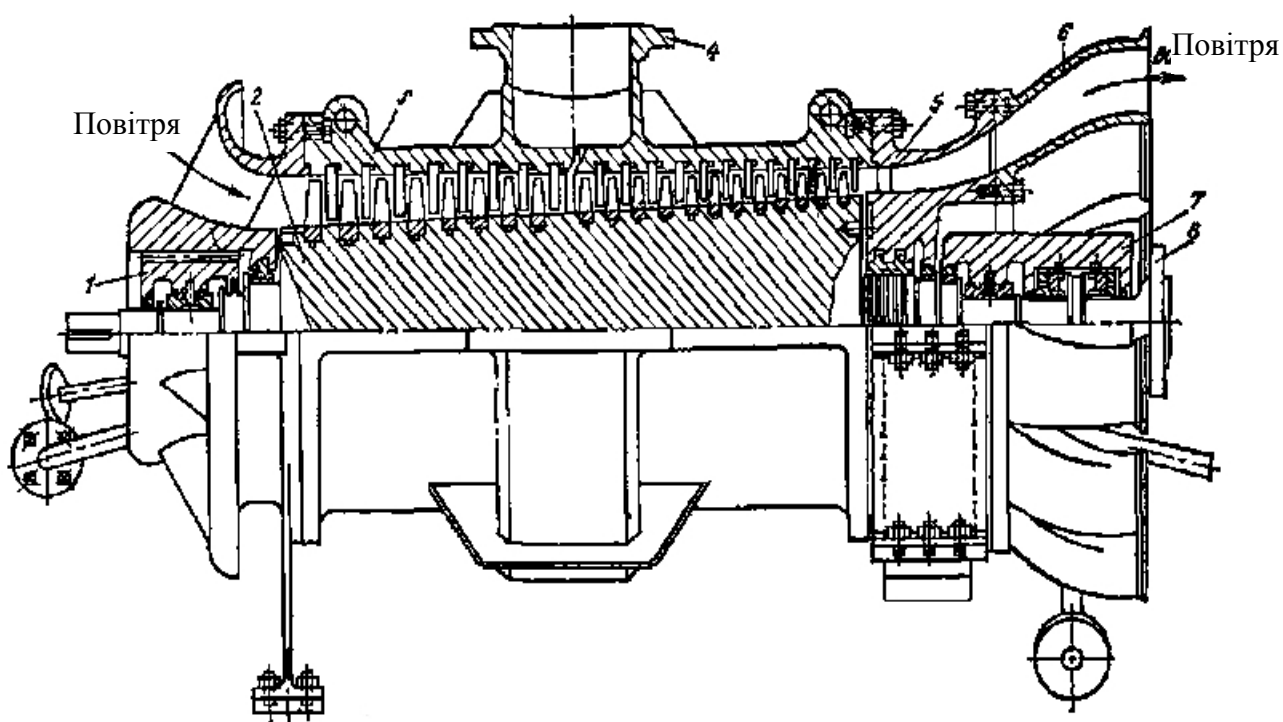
Осьовий компресор: 1 – опорний підшипник; 2 – барабан; 3 – корпус; 4 – патрубок проміжного відбору; 5 – дифузор; 6 – перехідні патрубки; 7 – опорно-упорний підшипник; 8 – фланець жорсткої муфти.
